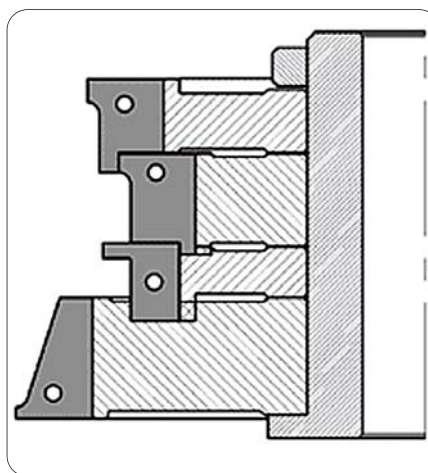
Сборная фреза концерна «Удача» с профильными однокромочными пластинами
